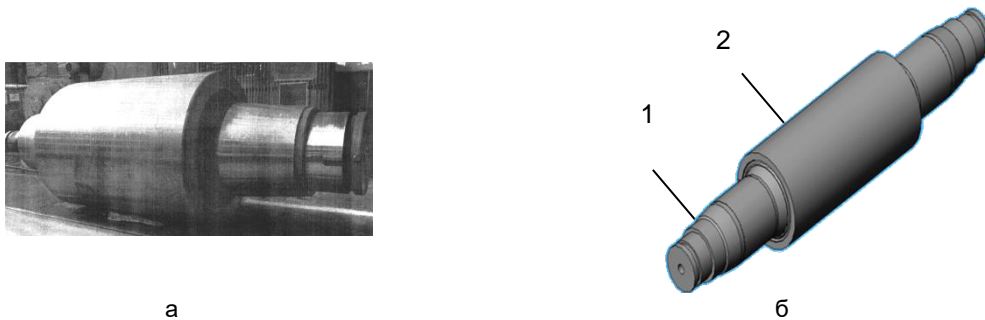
Общий вид (а) и схема (б) конструкции составного прокатного валка: 1 – ось валка; 2 – бандаж;
